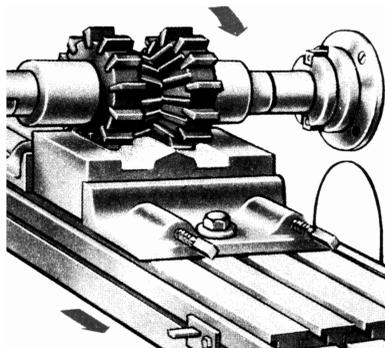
Фрезерование фасонной поверхности набором фрез
